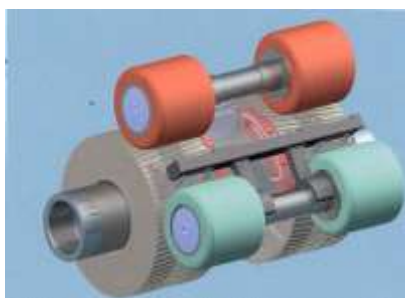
Общий вид пневматической колект установки для выработки пряжи.
